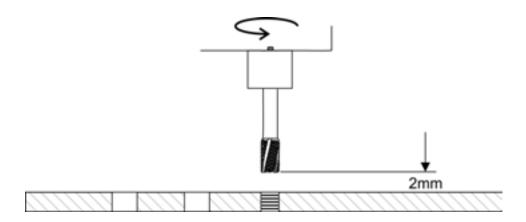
Abstand von der Spitze des Gewindeformwerkzeugs zum Werkstück
